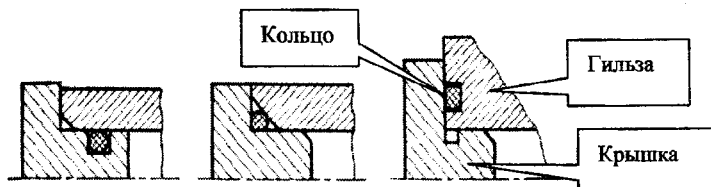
Варианты уплотнения неподвижных соединений крышки и гильзы пневмоцилиндра резиновыми кольцами
